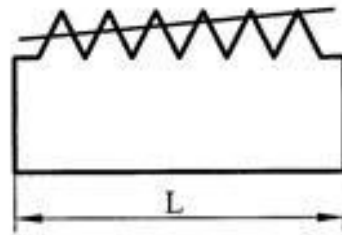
Схема образования зубьев резьбовой гребенки
